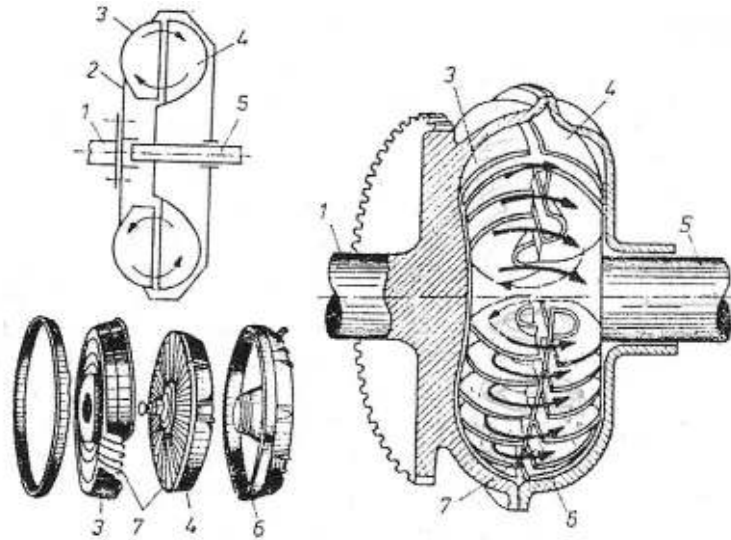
Ambreiaj hidraulic 1-arbore cotit; 2-flansa; 3-rotorul pompei; 4-rotorul turbinei; 5-arborele primar al cutiei de viteze; 6-carcasa; 7-palete.
